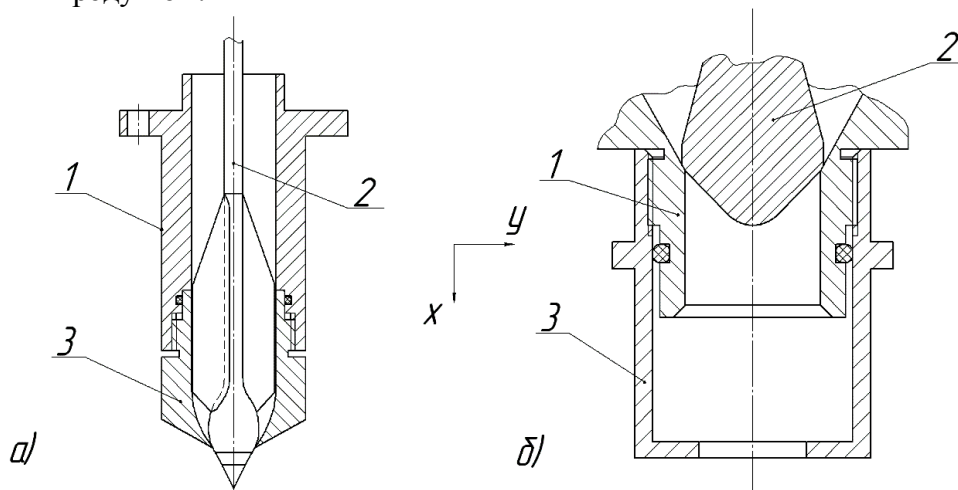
Конструкція робочого органу в дозаторах для рідких харчових продуктів: а) конічна; б) циліндрична: 1 – сідло; 2- клапан; 3 – корпус
